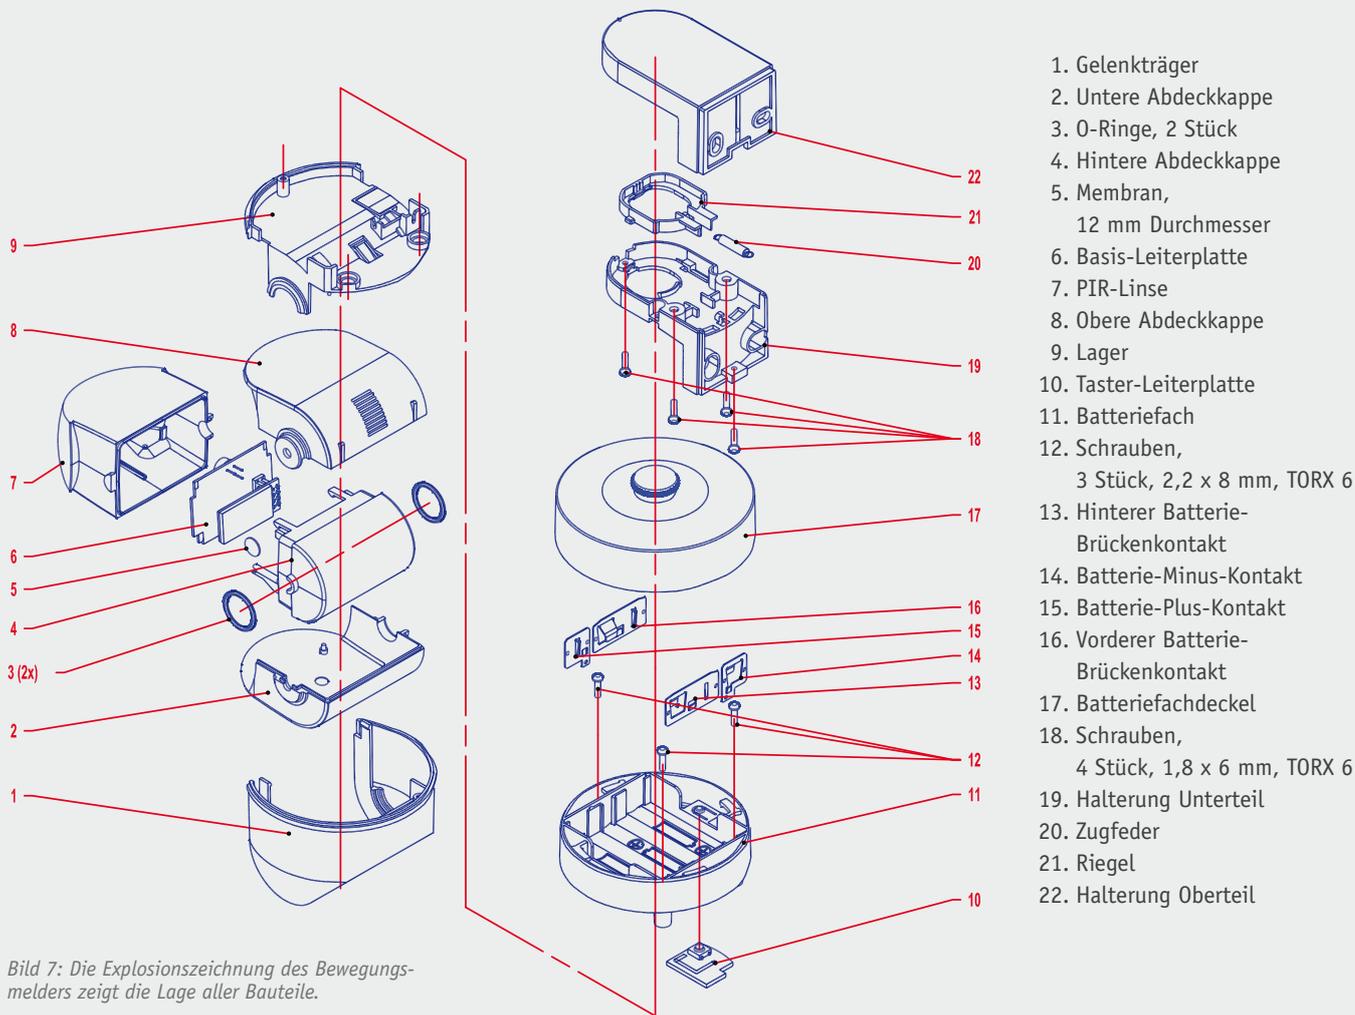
Die Explosionszeichnung des Bewegungsmelders zeigt die Lage aller Bauteile.
